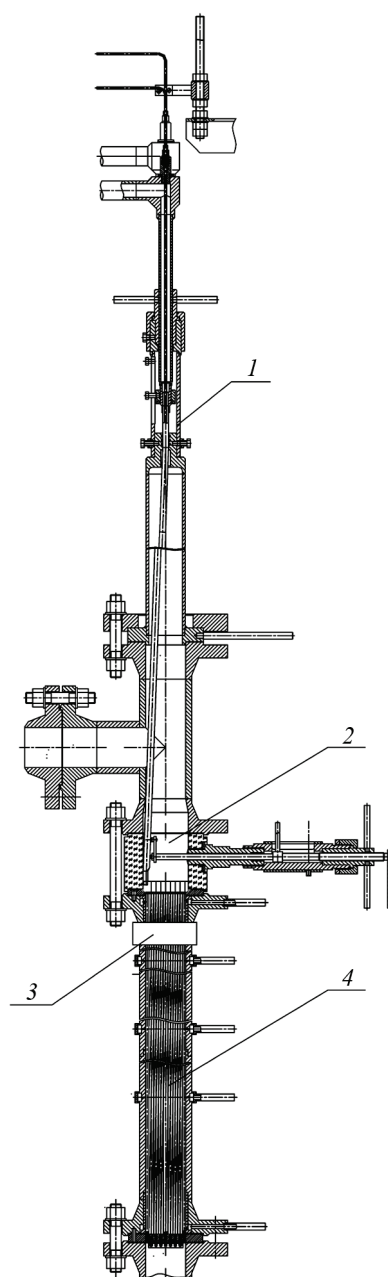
Общий вид модели РУ РБМК: 1 – устройство вертикального перемещения пробоотборника; 2 – устройство горизонтального перемещения пробоотборника; 3 – устройство отбора пристенной пленки; 4 – модель сборки
